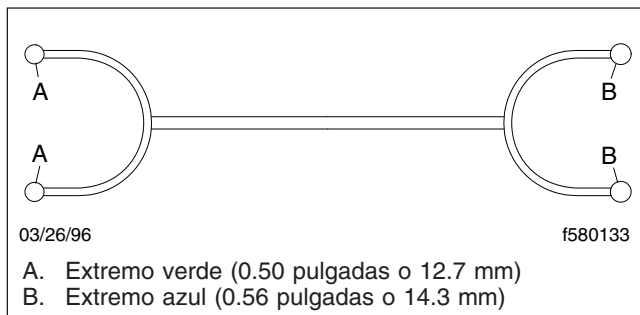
, Herramienta para el recorrido del collarín A02-12419-000
